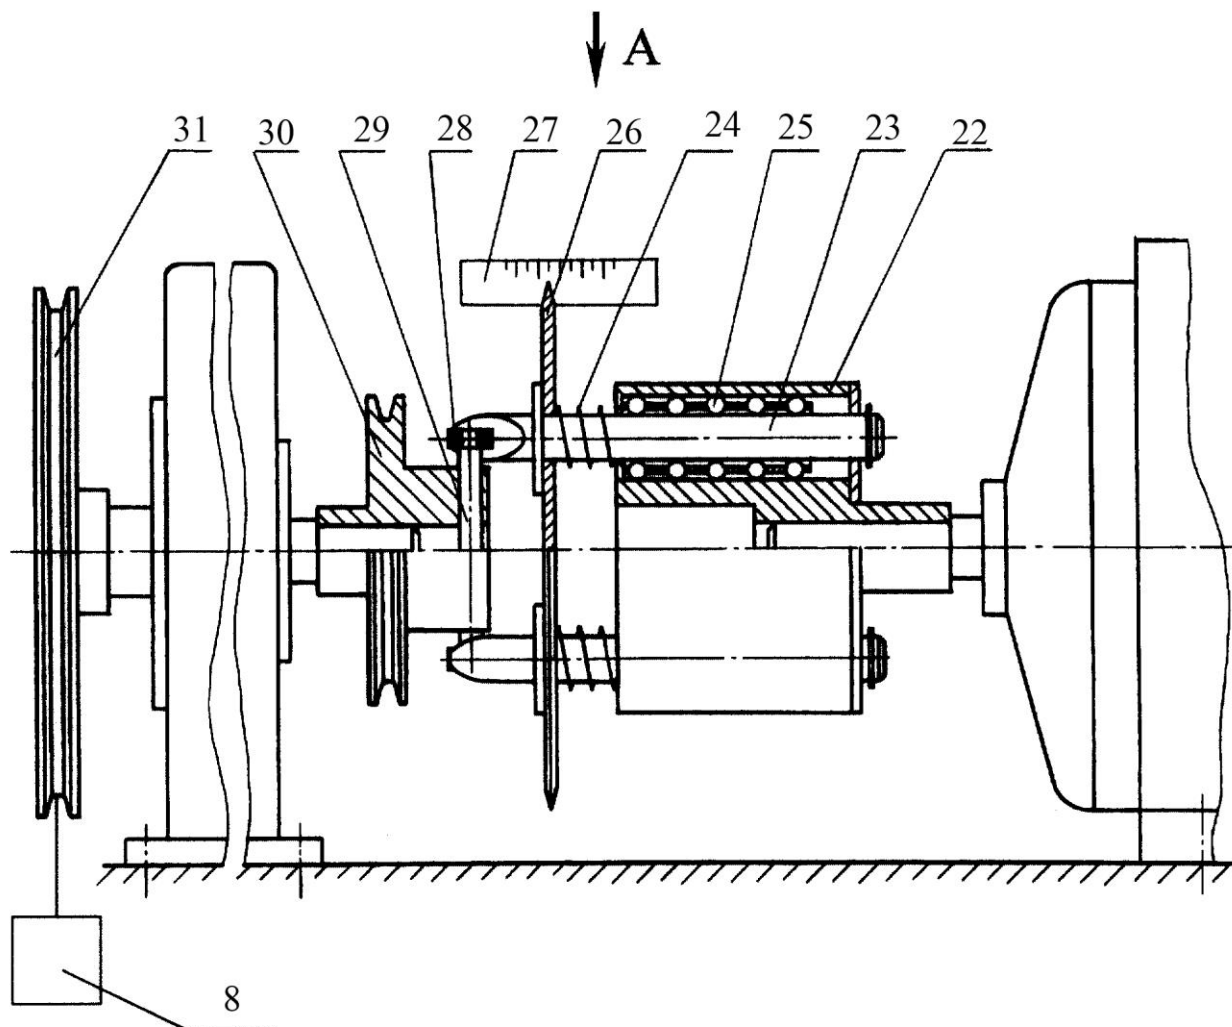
Загальний вигляд стенду для визначення ККД механічних передач
